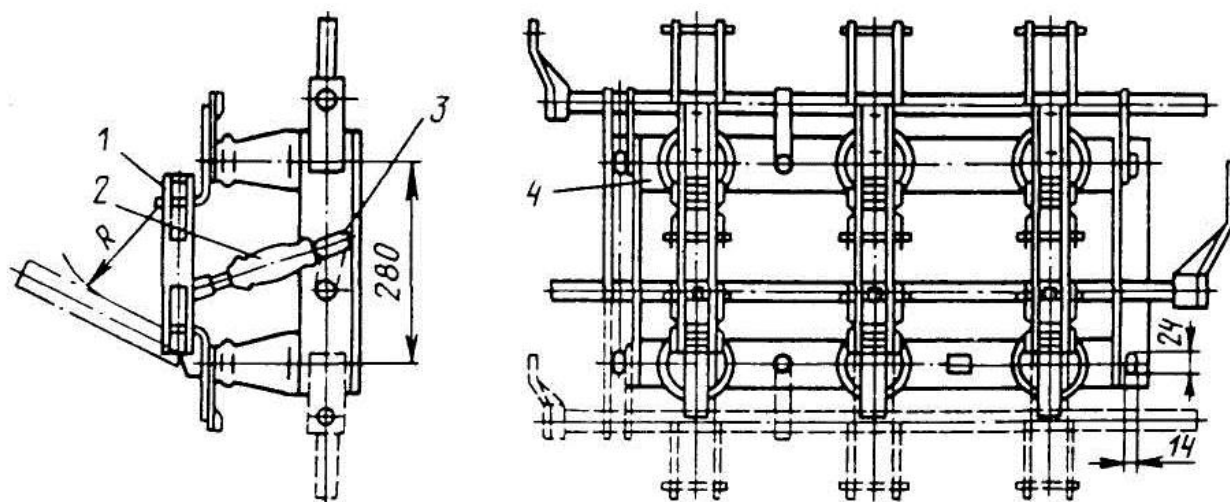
Разъединитель внутренней установки типа РВЗ–10/400:
